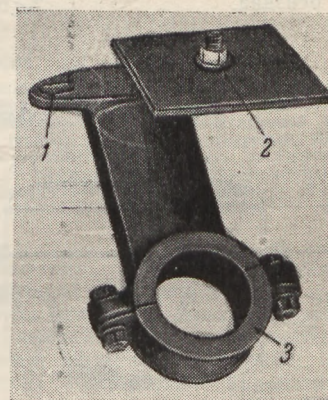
Верхний кронштейн рулевой колонки автомобиля ЯАЗ-200.
